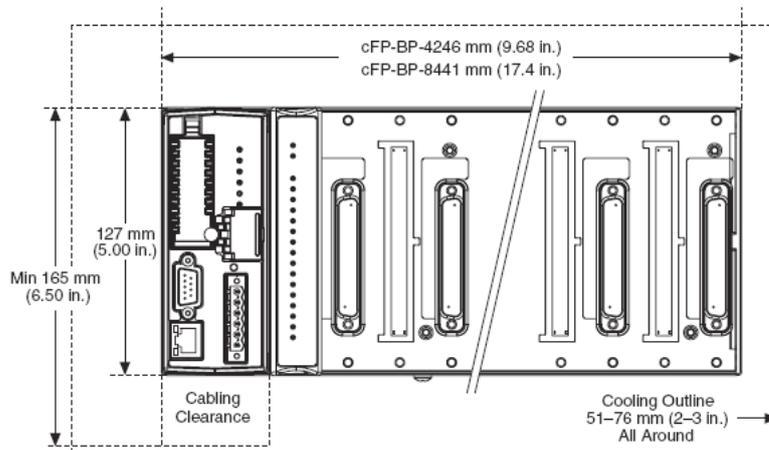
Respaldar cFP-BP-x con cFP-21xx instalado, vista frontal con dimensiones.
